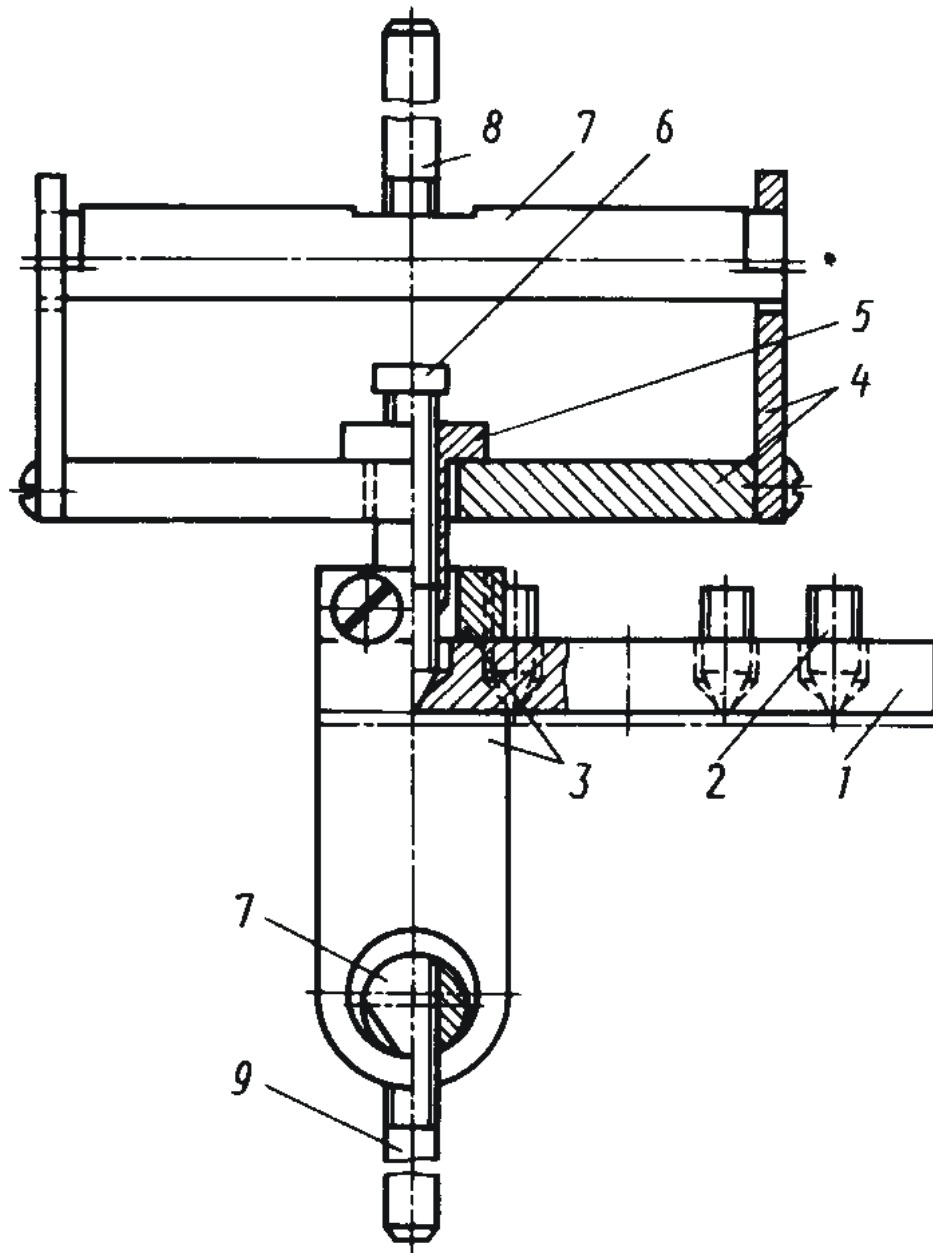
Конструкция приспособления для оценки адгезионной прочности покрытий:
